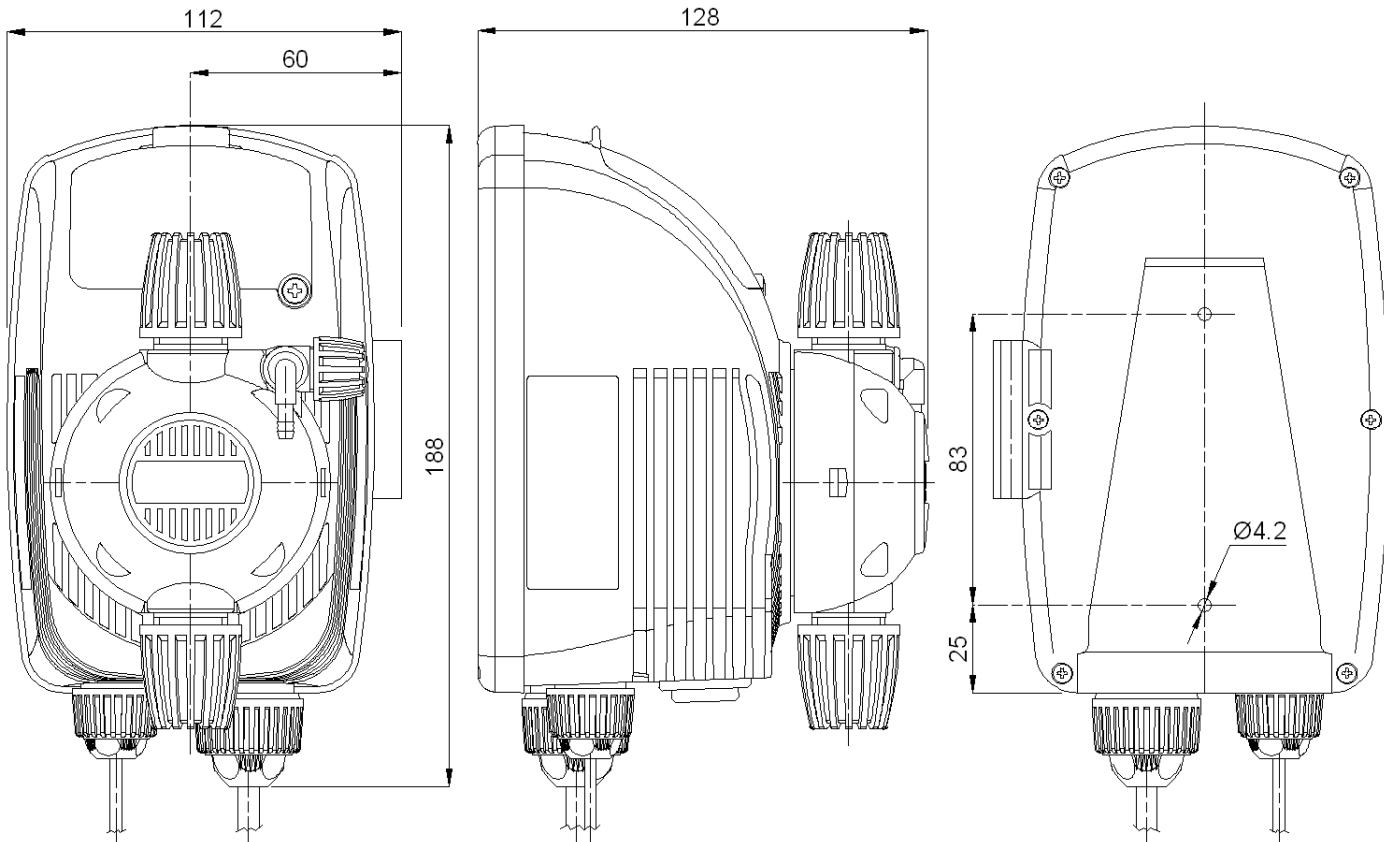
SERIE "HC 897" A MURO / WALL MOUNTING / VERSION A PAROI / VERSION A PARED/ НАСТЕННЫЙ
